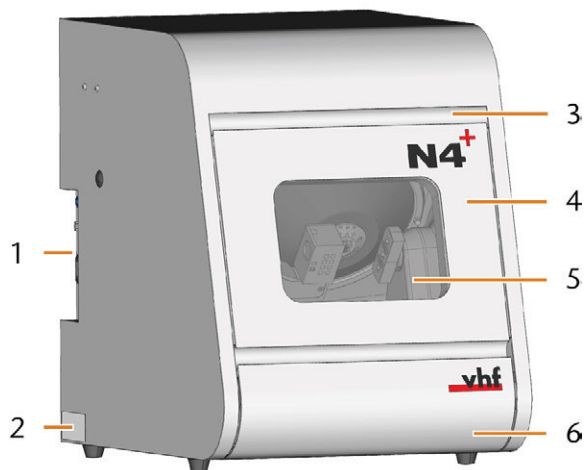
VISTA FRONTAL DE LA MÁQUINA
